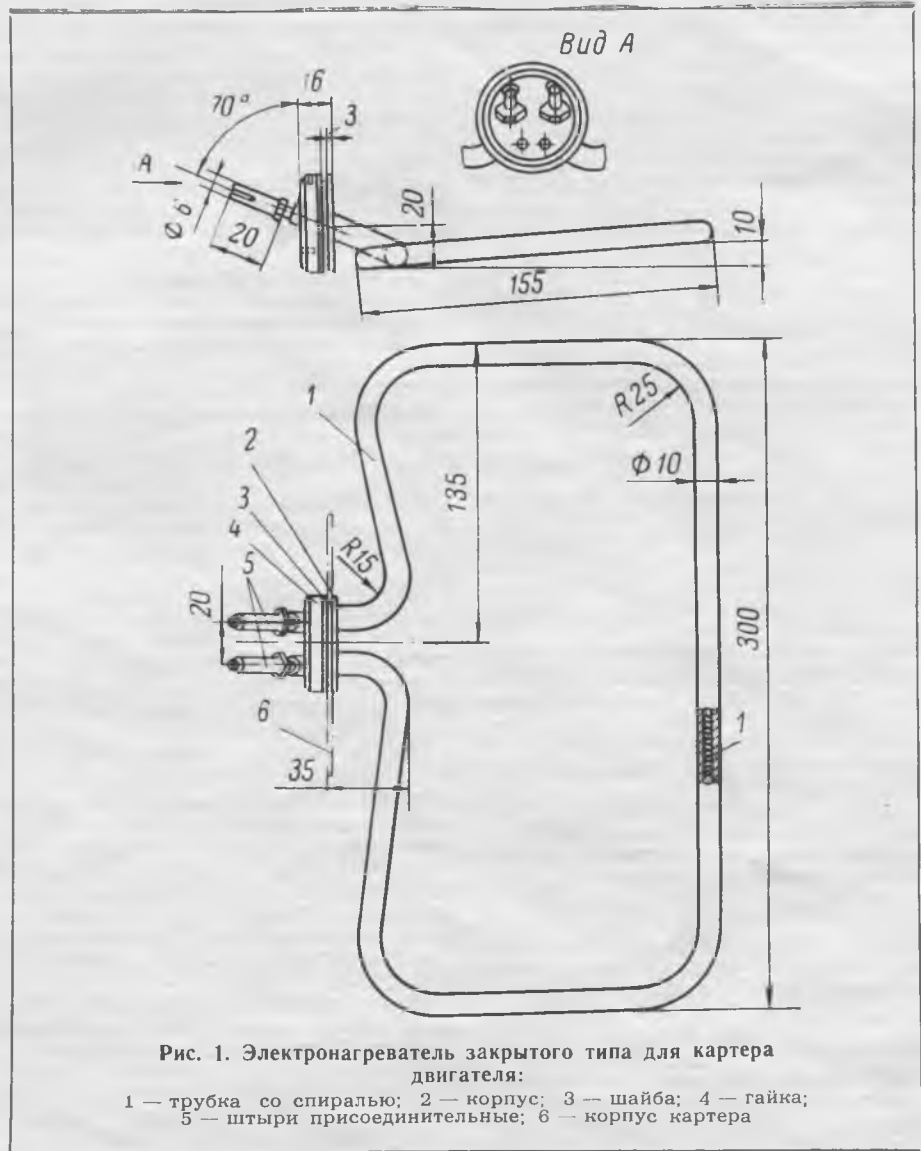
Электронагреватель закрытого типа для картера двигателя:
